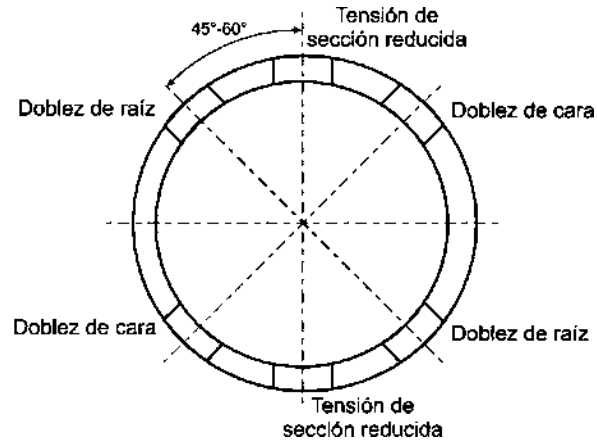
Seccionamiento de las uniones soldadas disímiles ^[118].
